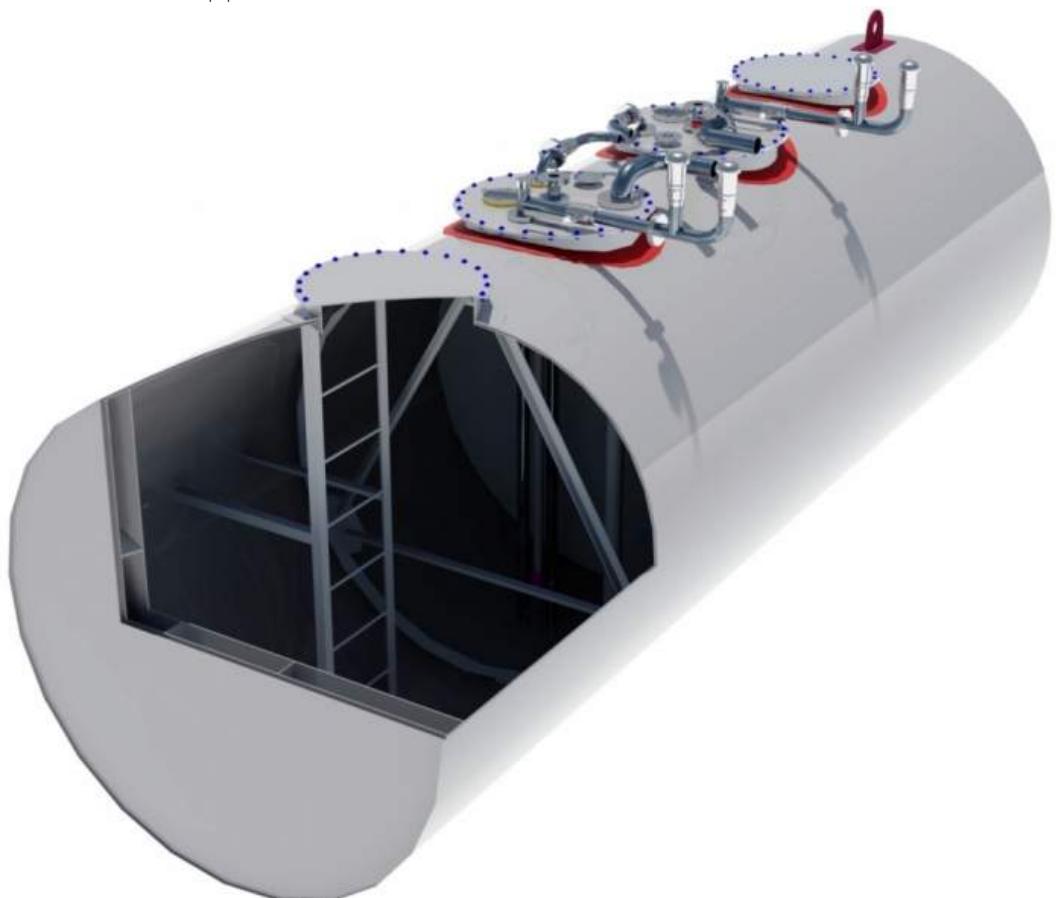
Внешний вид горизонтального цилиндрического резервуара
